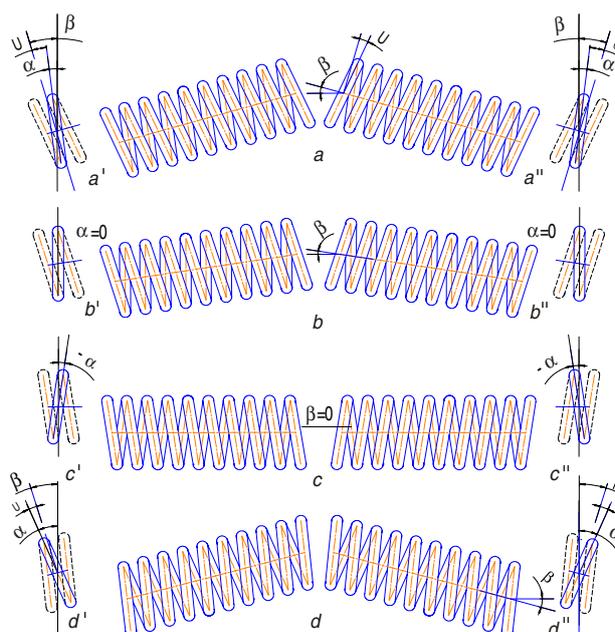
Схемы возможных расположений секций спирального пневматического катка относительно направления движения агрегата
